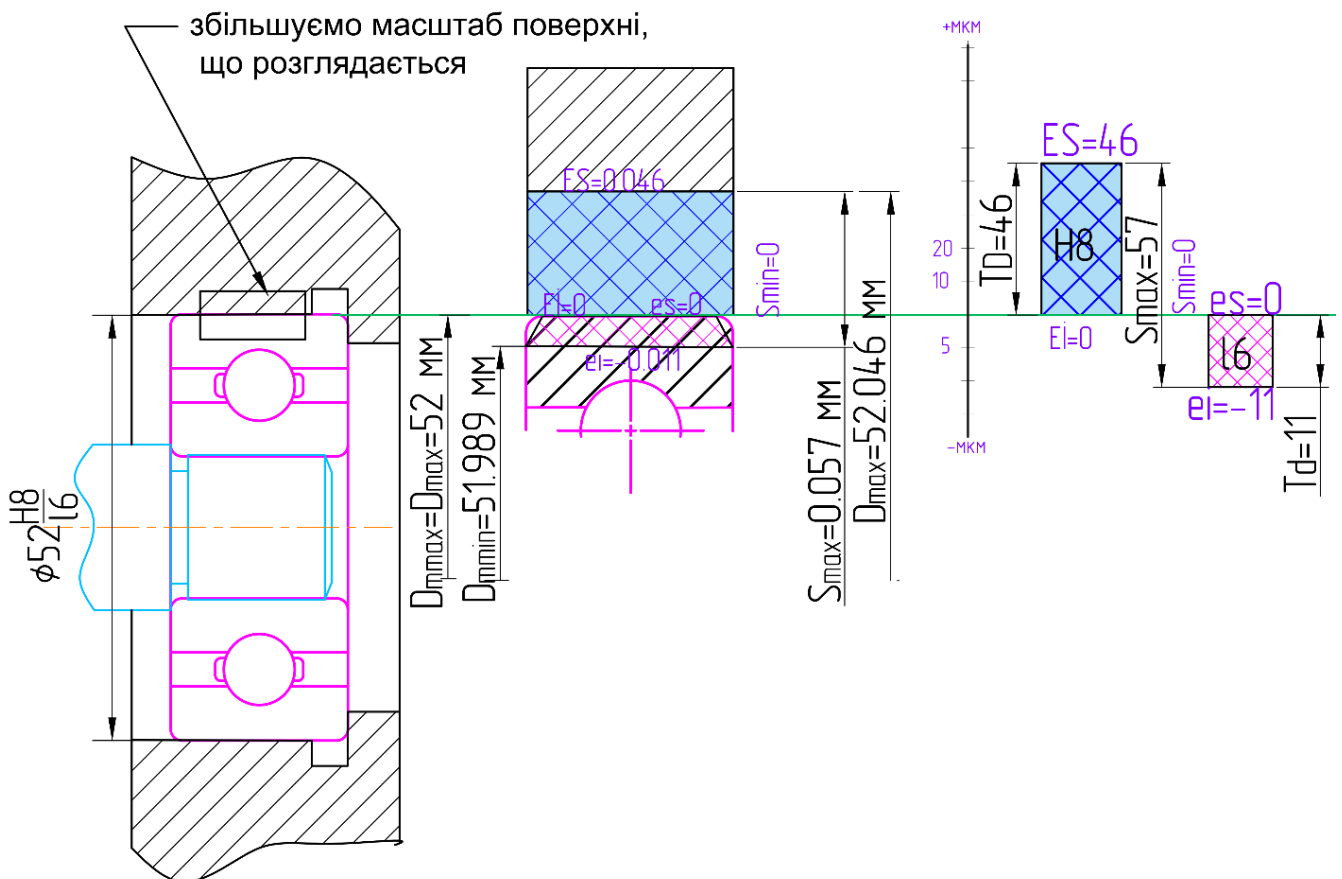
Схема розташування полів допусків для з'єднання підшипника з корпусом $\phi 52 \frac{H8}{f6}$ (*Виконується на форматі А1 див. додаток Б2)
